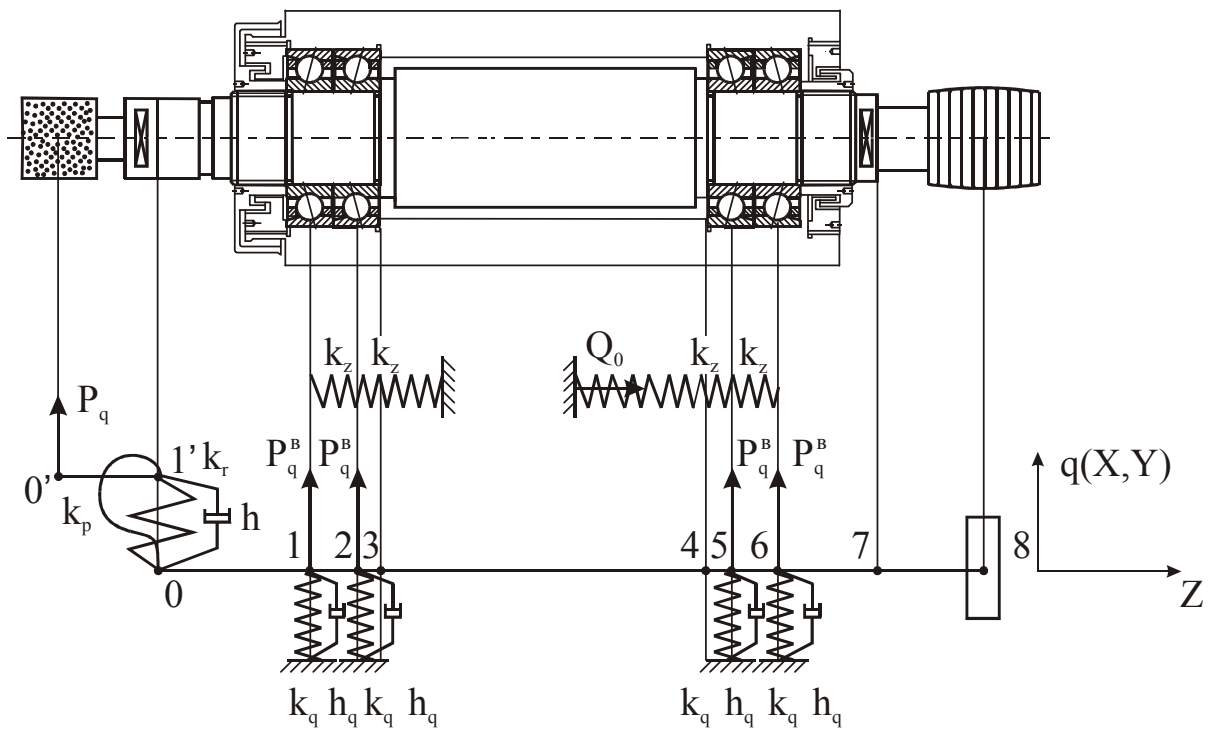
Конструктивна і розрахункова схеми пружної системи “шпиндель – оправка”
